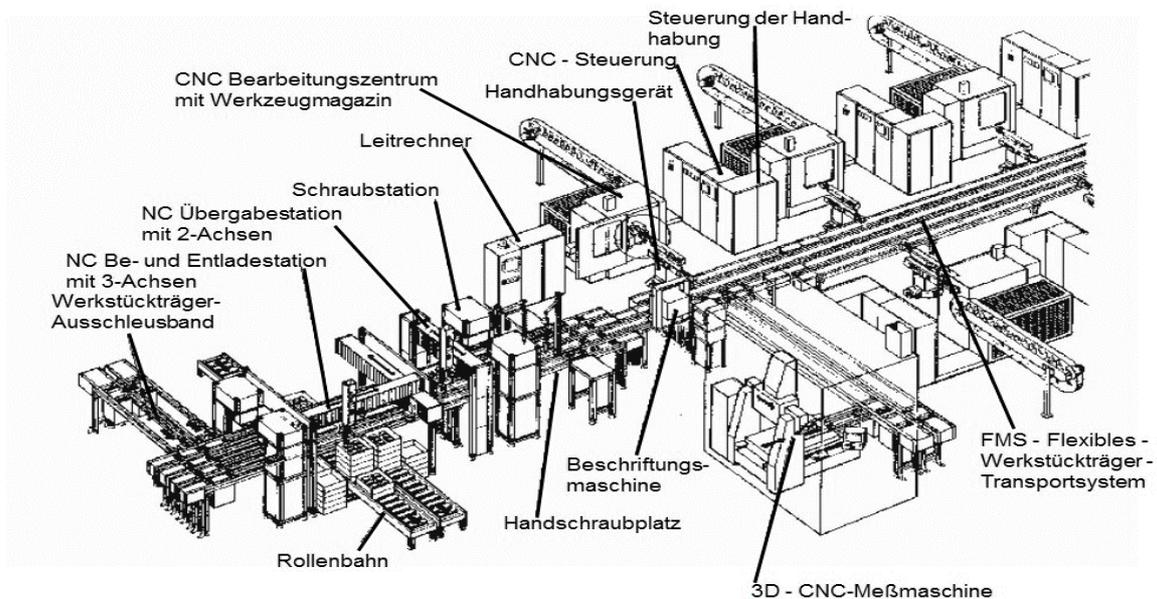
Elemente und Grundaufbau eines FFS ^[1]
